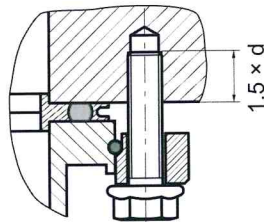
Flanschverbindung ISO-K zu ISO-F, Sechskantschraube und Gewindebohrung
